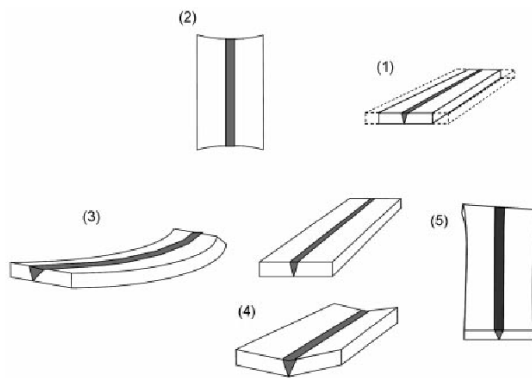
Tipos de distorsión provocados por el proceso de soldadura. [10]
